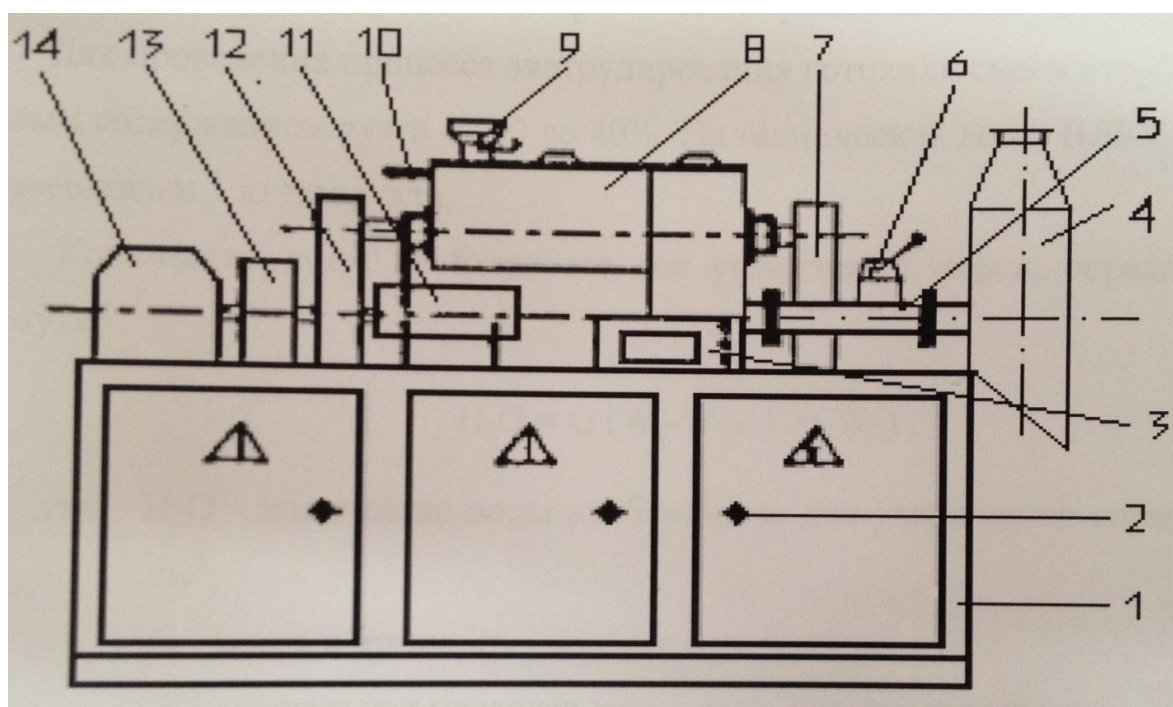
Схема универсального пресс-экструдера. 1 – станина; 2 – замок двери; 3 – пульт управления; 4 – кожух режущего механизма; 5 – рабочий цилиндр прессующего узла; 6 – муфта сцепления; 7 – ограждение привода режущего механизма; 8 – месильное корыто; 9 – питающий бункер; 10 – штуцер привода воды; 11 – подшипниковый узел прессующего механизма; 12 – ограждение привода вала месильного корыта; 13 – ограждение муфты; 14 – редуктор.
